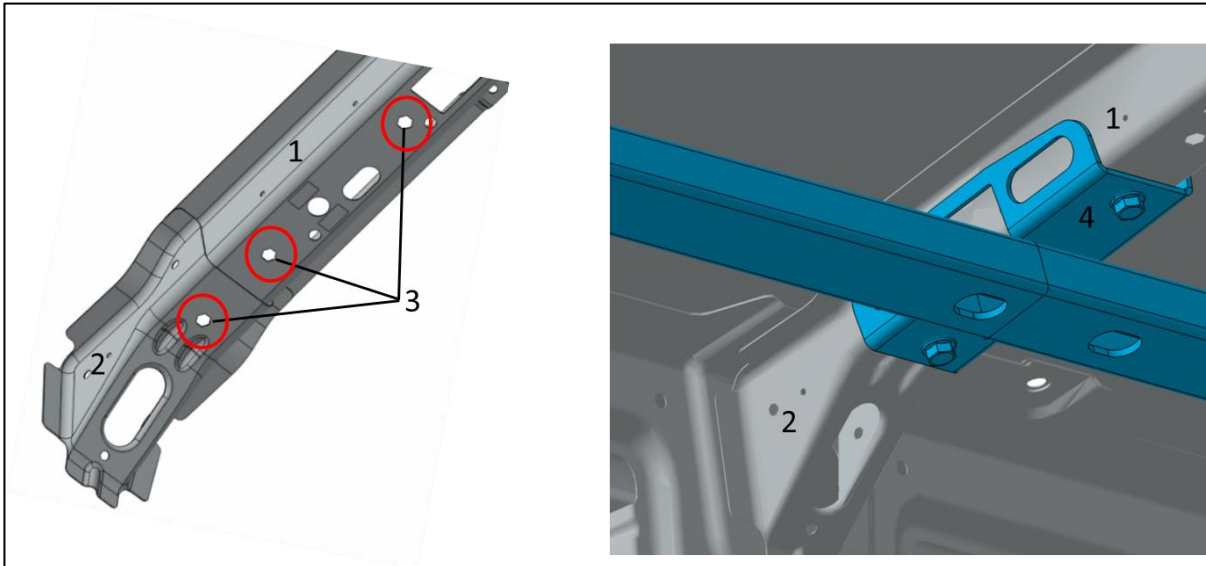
esempio "collegamento profilato lungo sul tetto del veicolo"
